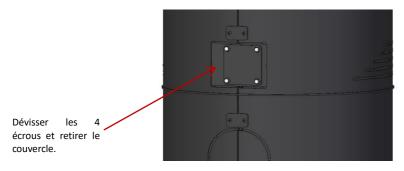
Vue arrière de l'équipement, retirer le couvercle du sas extérieur
